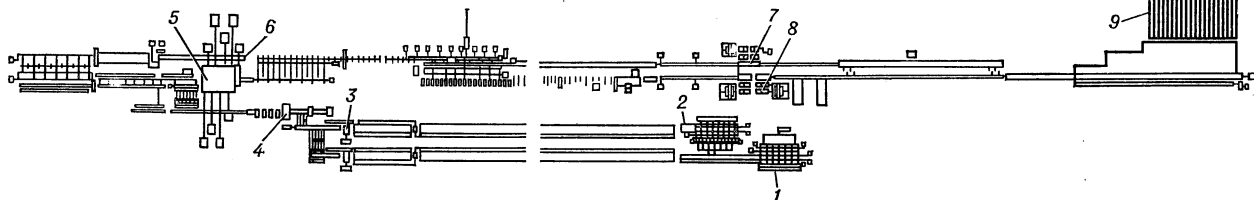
Схема расположения оборудования трубопрокатного агрегата с непрерывным удлинительным станом: 1 — загрузочное устройство секционных печей; 2 — рольганг перед нагревательной печью; 3 — ножницы; 4 — рабочая клеть прошивного стана; 5 — непрерывный стан; 6 — извлекатель оправки; 7 — одиннадцатиклетевый калибровочный стан; 8 — девятнадцатиклетевый редуционный стан; 9 — холодильник.
